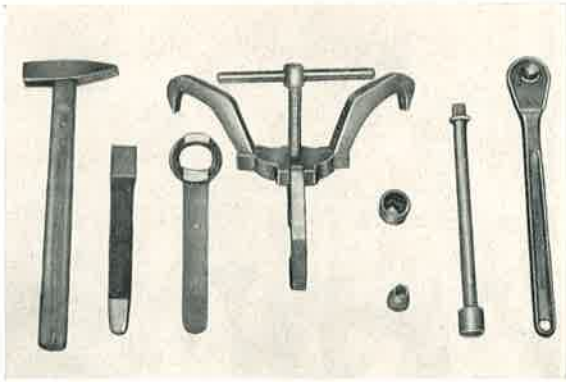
Zusammenstellung der Werkzeuge, die für die Arbeit der Gruppe M, Motor, M 28 gebraucht werden.
